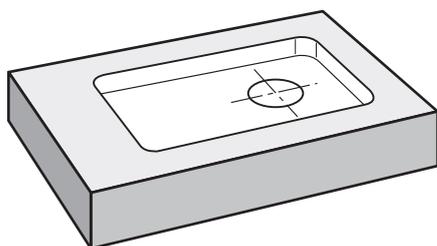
Образцовая деталь – Изготовление посадочного места
